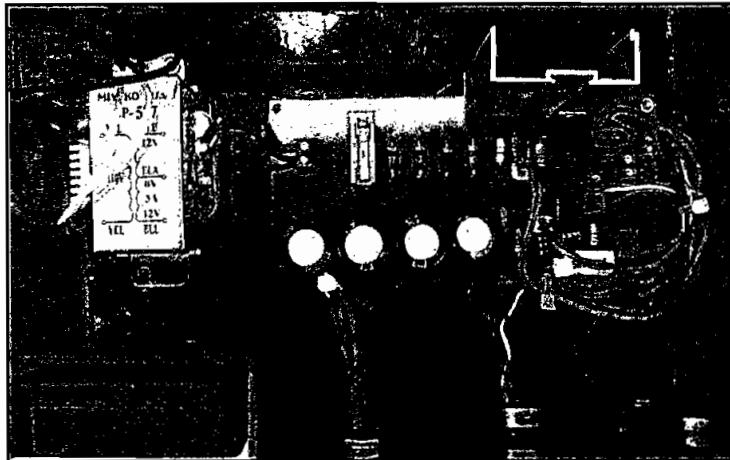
Placa para la Fuente Regulada de Voltaje con Realimentación
